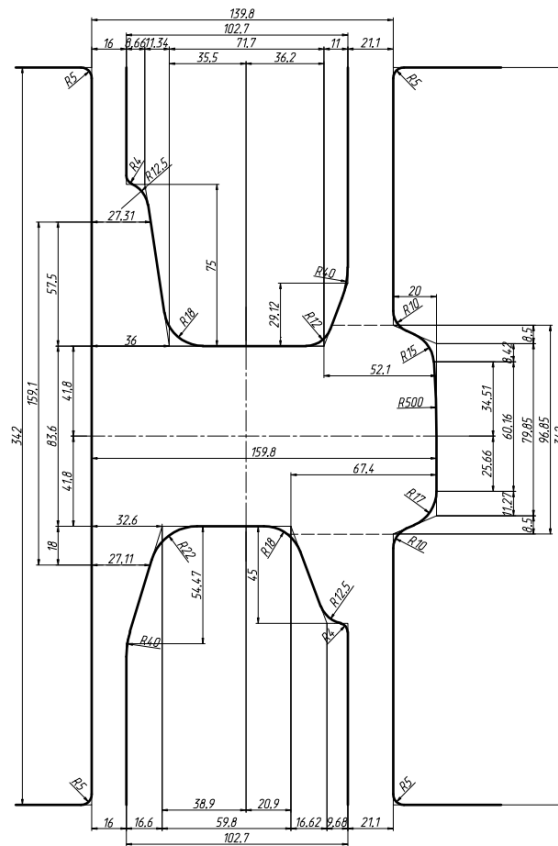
Размеры первого по схеме прокатки универсального четырехвалкового калибра
